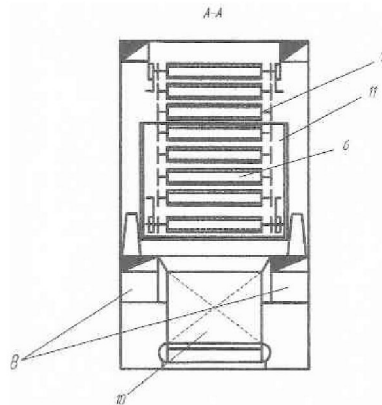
Розріз А-А агрегата для термічної обробки
